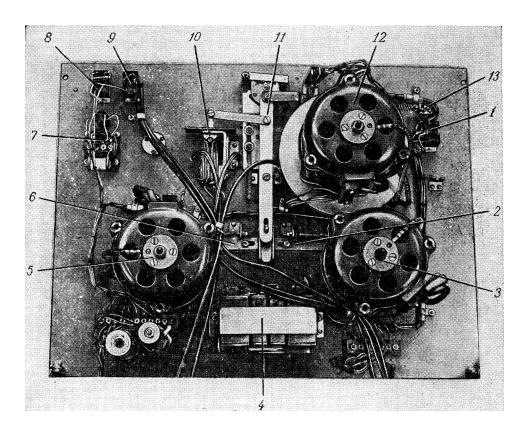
Расположение деталей на плате лентопротяжного механизма.
